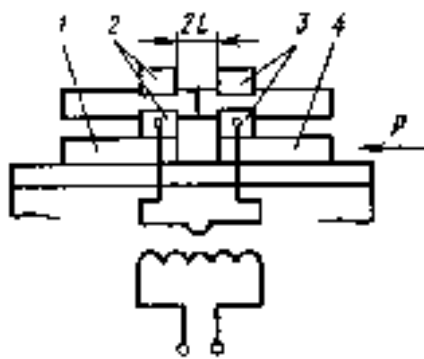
Схема контактной стыковой сварки
